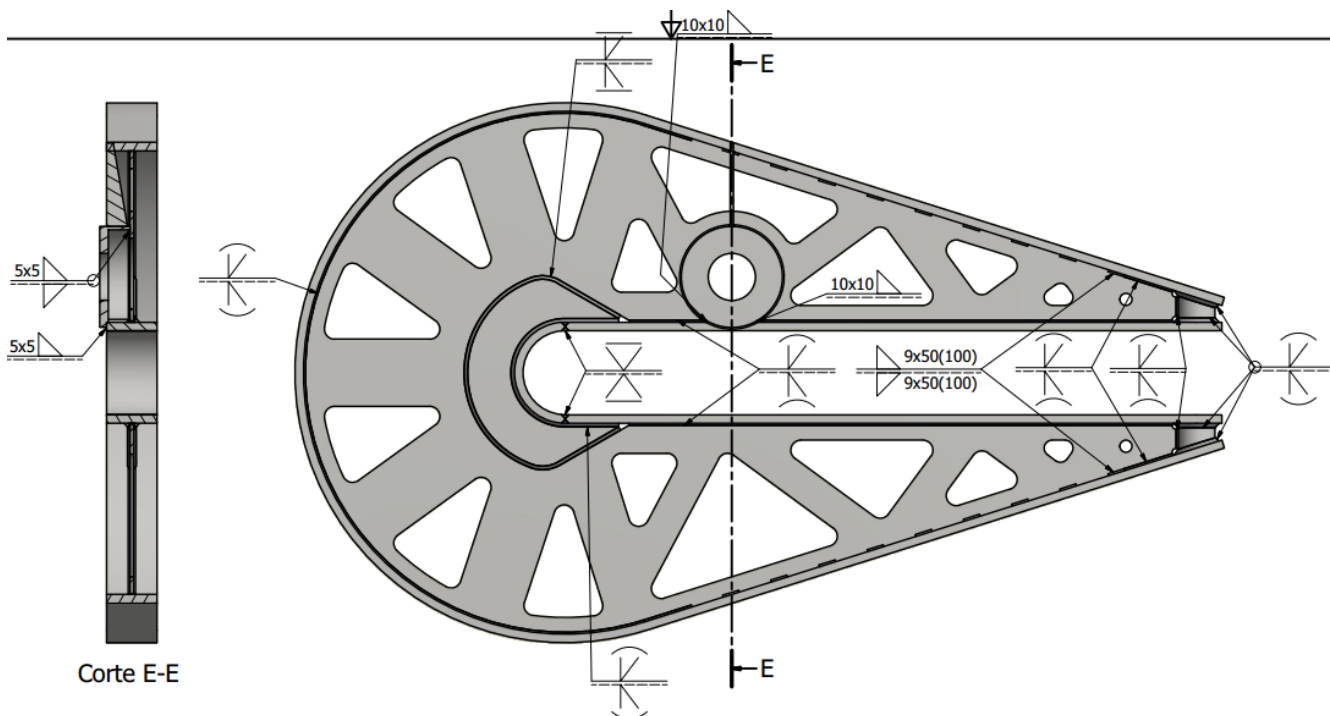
DIMENSÕES DOS PASSES DE RAIZ DOS CORDÕES DE SOLDA.
